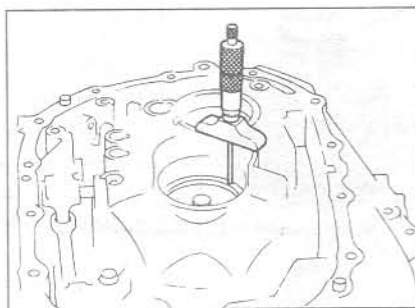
Предварительный натяг подшипника выходного вала - размер 'В' (Глава 15)
